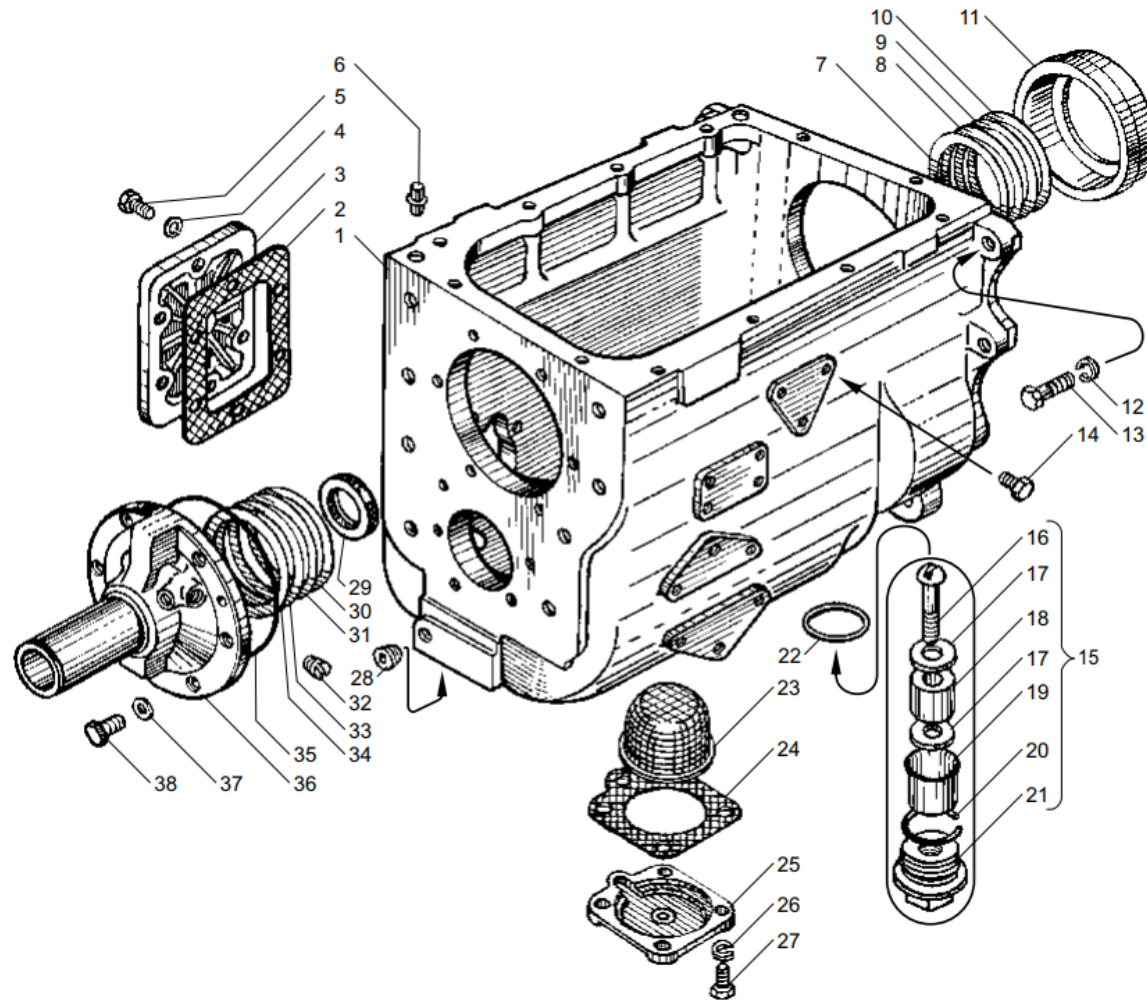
КАРТЕР КОРОБКИ ПЕРЕДАЧ
